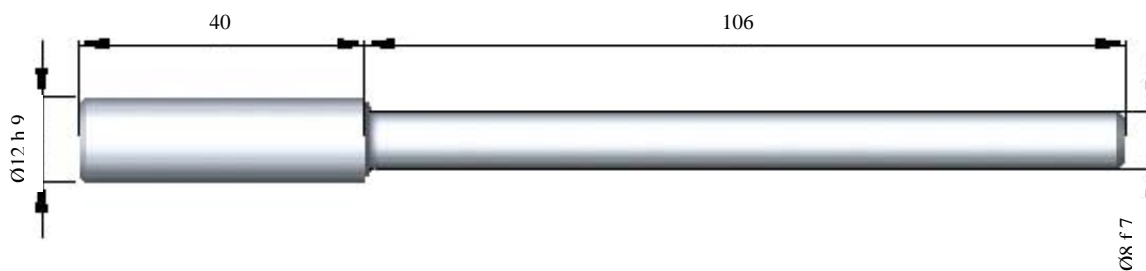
Géométrie de l'éprouvette usinée pour les essais de fatigue
